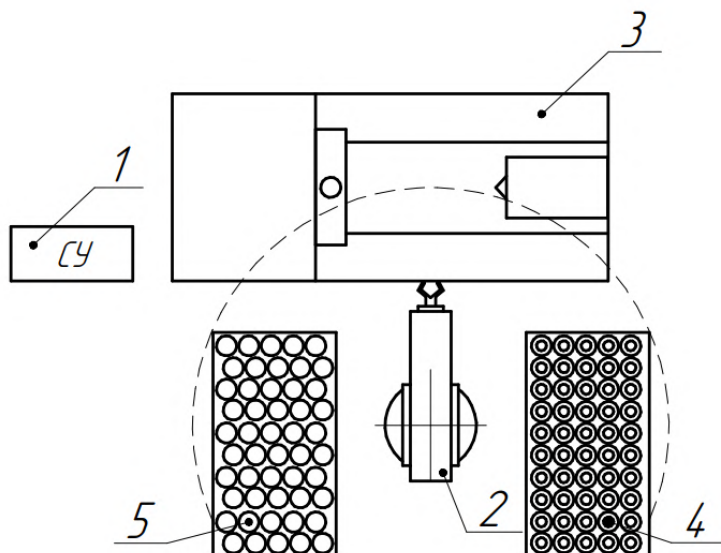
Компонировка гибкого производственного модуля (1 – Система управления; 2 – промышленный робот; 3 – станок; 4 – стол обработанных деталей; 5 – стол для заготовок)
